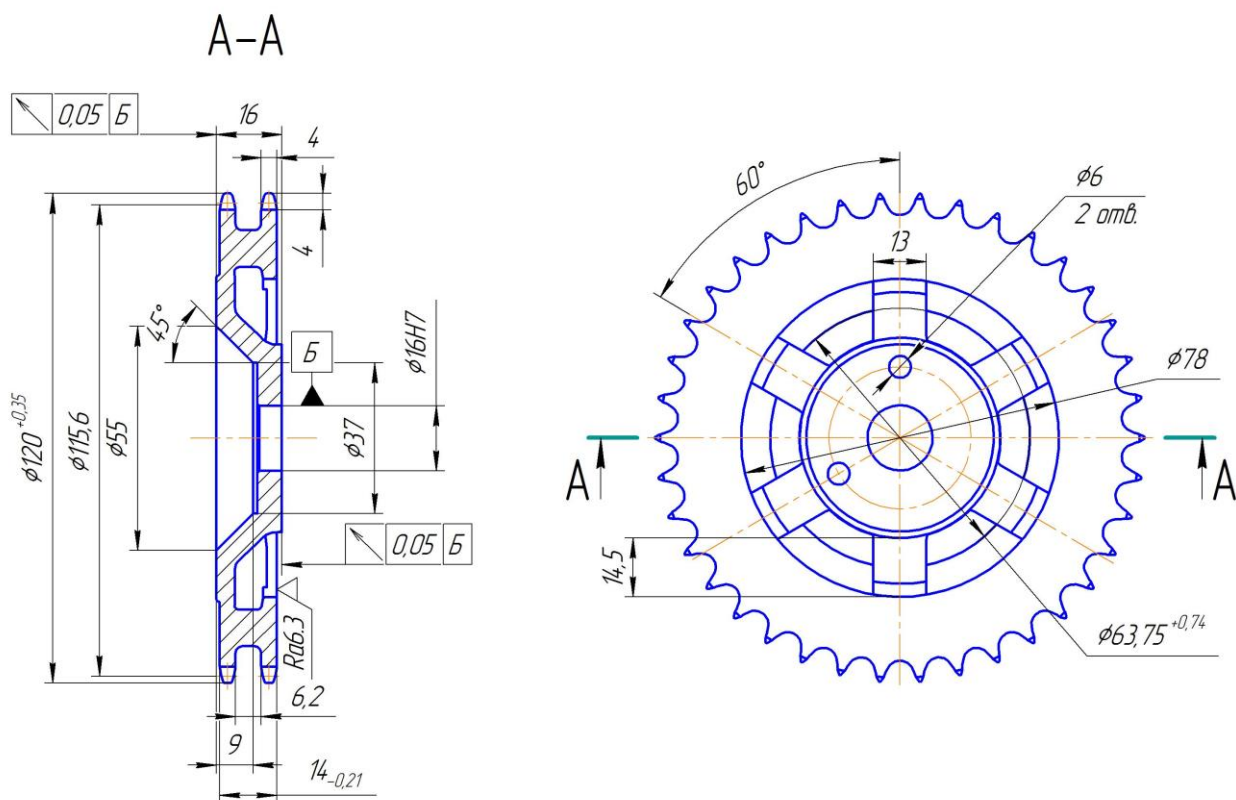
Зірочка приводу розподільного вала двигуна ВАЗ-2101
